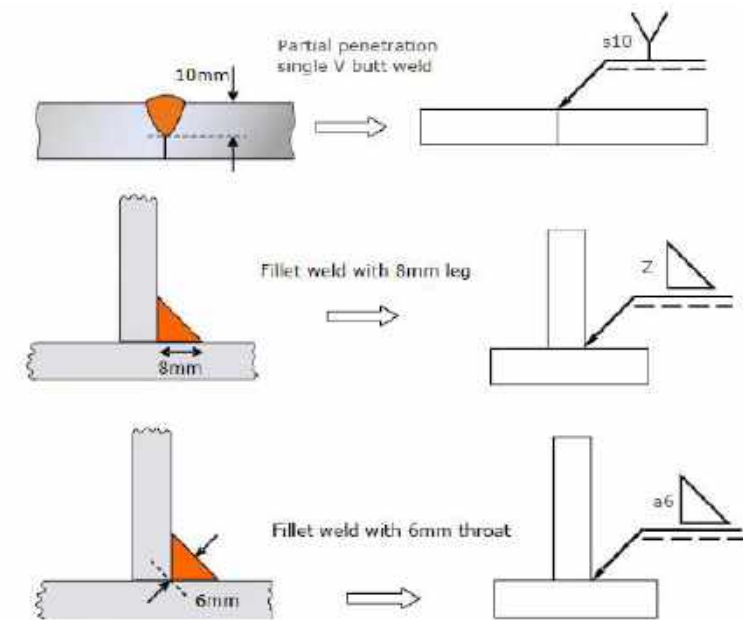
simbol las *Deep penetration weld* dengan standar ISO (dimensi dalam millimeter).
